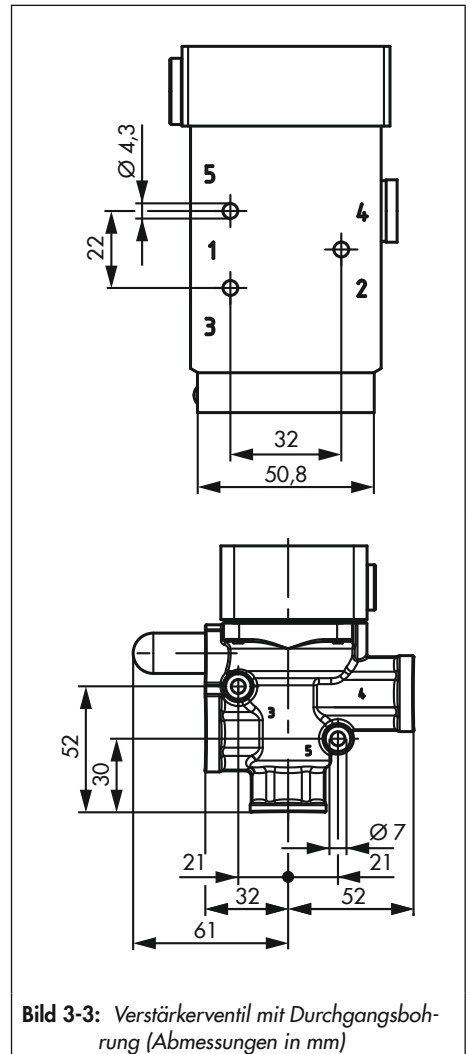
Verstärkerventil mit Durchgangsbohrung (Abmessungen in mm)
